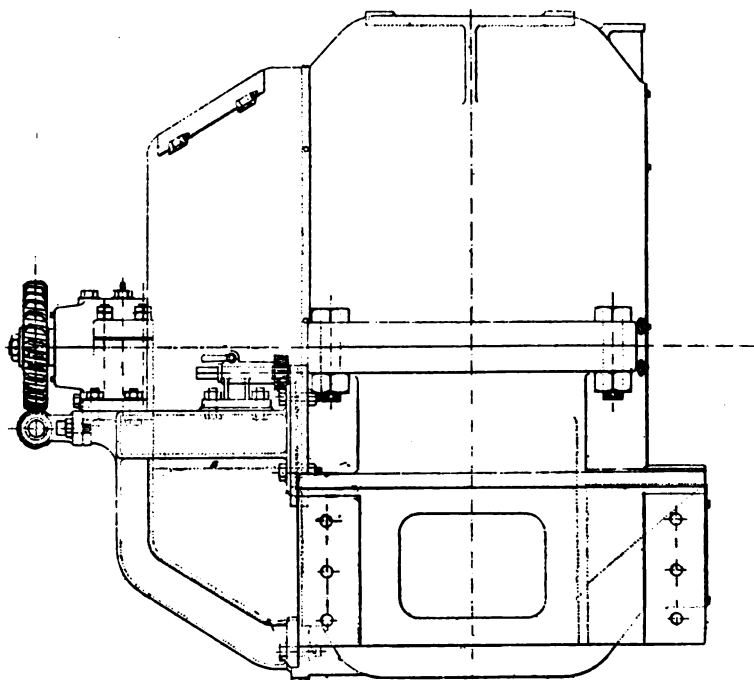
à 235. — Vue d'ensemble de la machine à vapeur équilibrée, à six lignes de cylindre.
